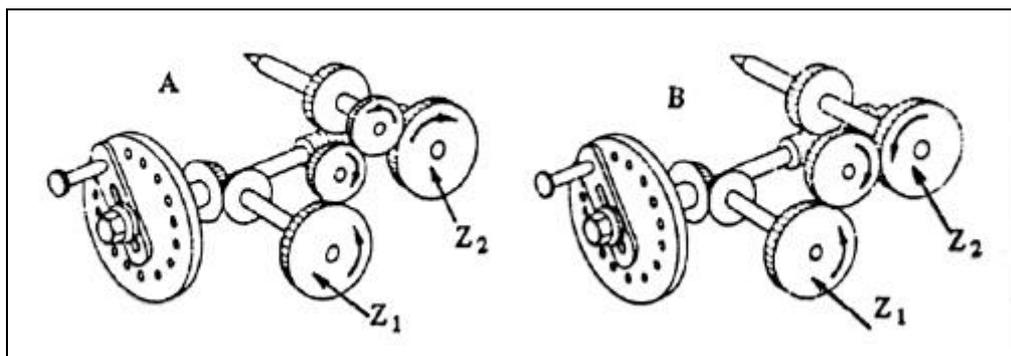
Esquema geral com a montagem de um trem simples.
